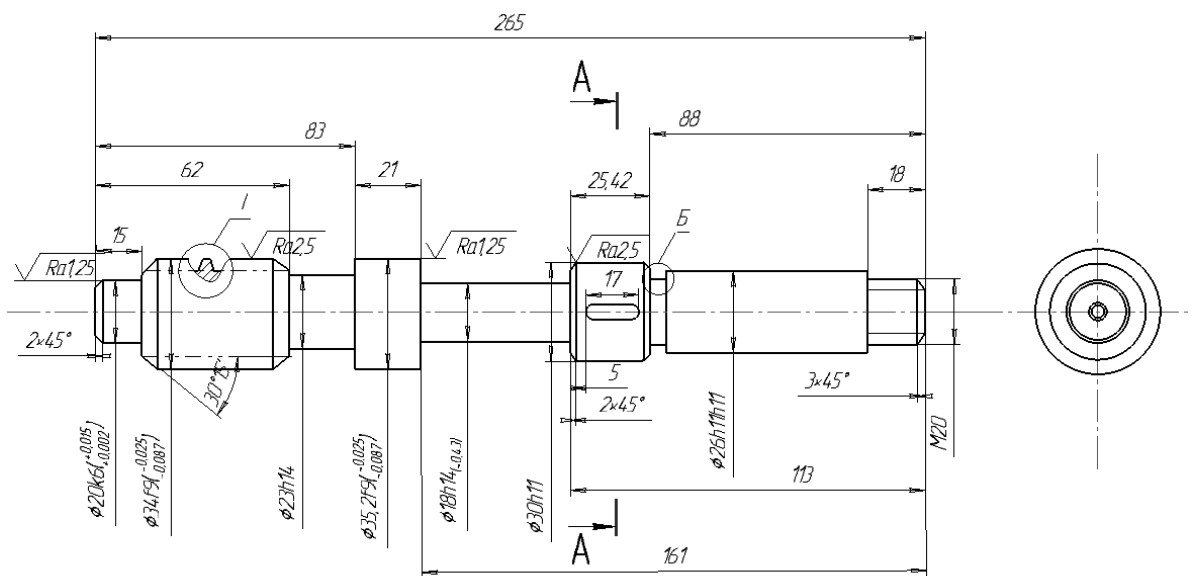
Ескіз деталі Вал черв'ячний
